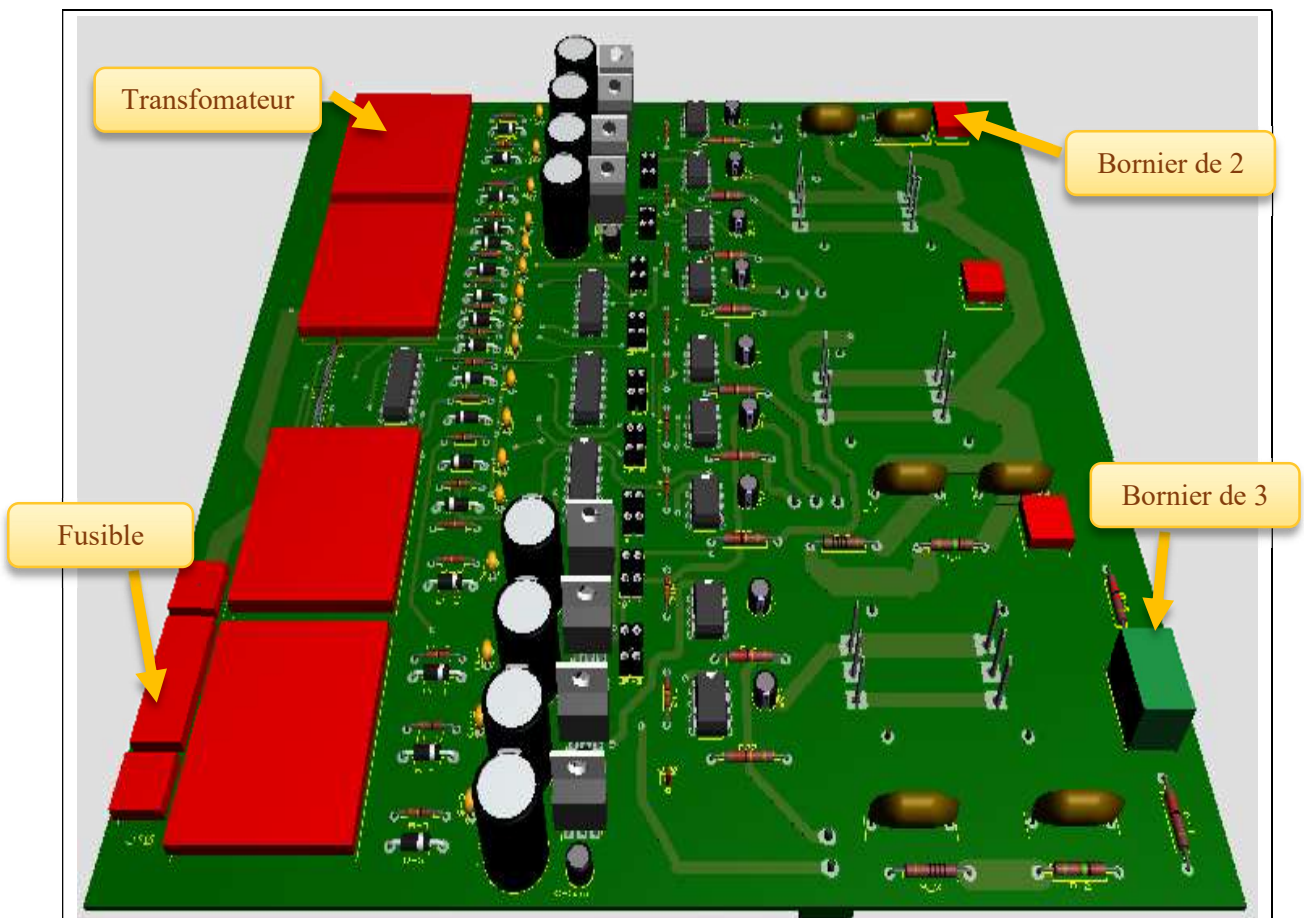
Vue en 3 Dimensions du PCB T-NPC 3N.
